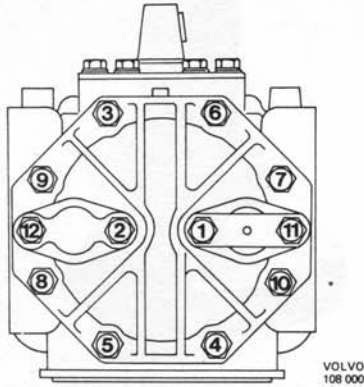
Anziehfolge für Zylinderkopfschrauben
